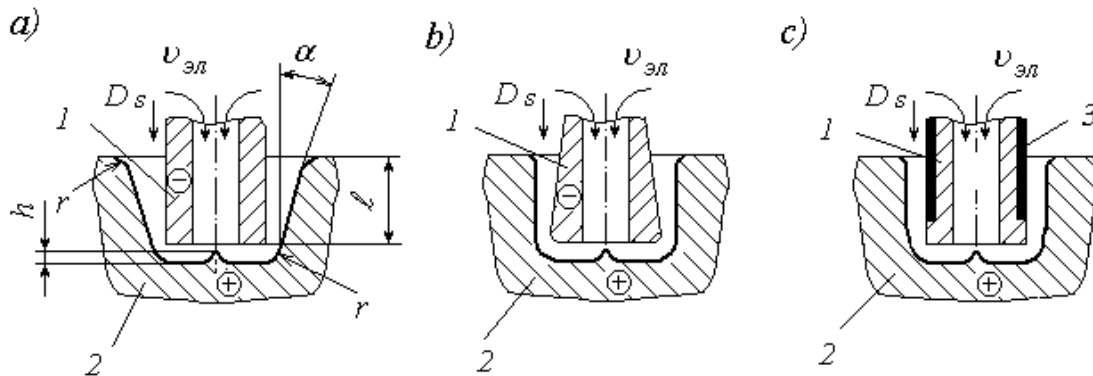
Погрешности формы прошиваемого отверстия (*a*) и способы её снижения (*b, c*): 1 — электрод-инструмент; 2 — заготовка; 3 — изоляционный материал
